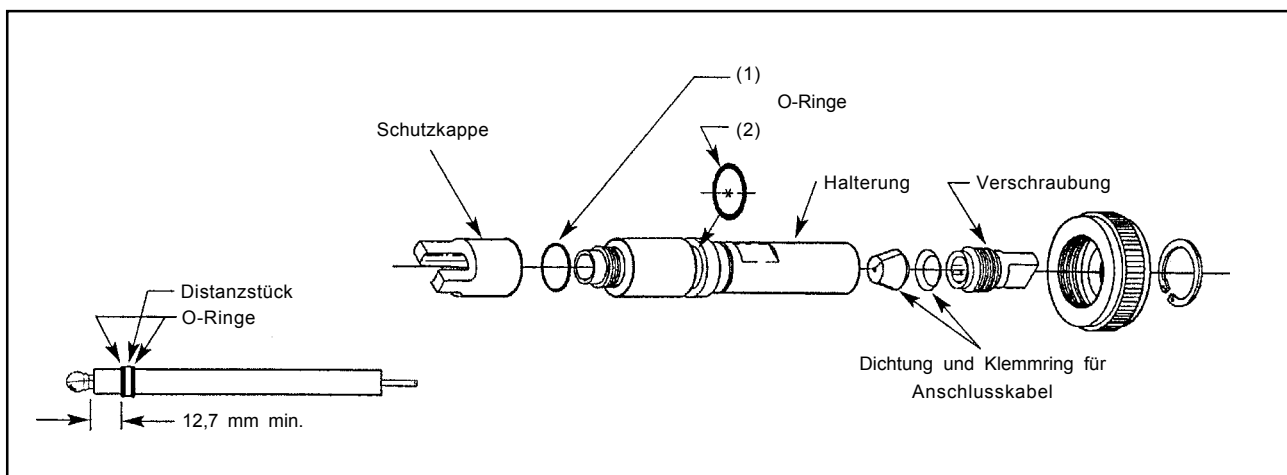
Explosionszeichnung Montageadapter P/N 22294-00
